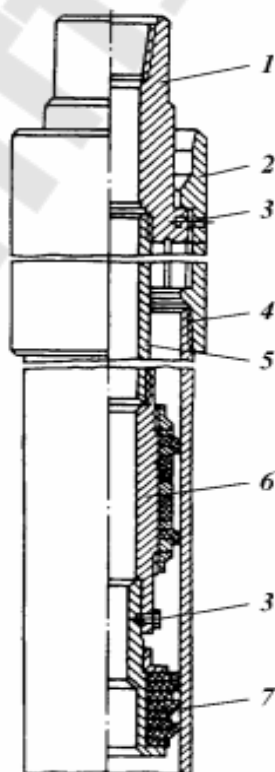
Кулачковый разъединитель: 1 – ниппель с кулачками; 2 – муфта с пазами; 3 – штифт; 4 – обсадные трубы спускаемого хвостовика; 5 – несущая
